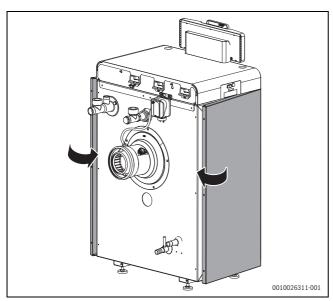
Pousser les panneaux latéraux par-delà le panneau arrière de la chaudière
